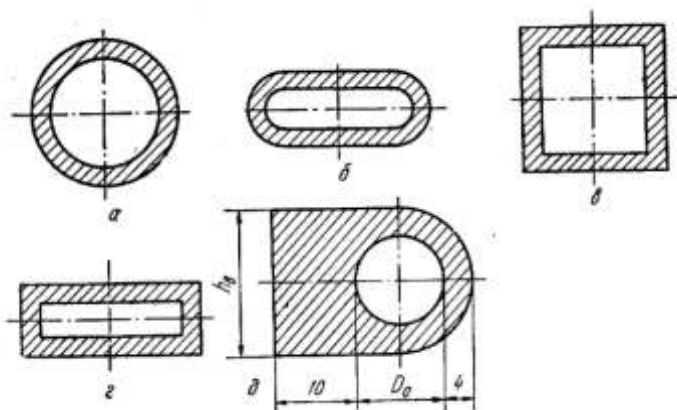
Профили трубки индуктора: а) - круглый (ГОСТ 617-72); б) -овальный; в) -квадратный (ГОСТ 16774-71); г) - прямоугольный (ГОСТ 16774-71); д) — неравноценный (D -образный)
